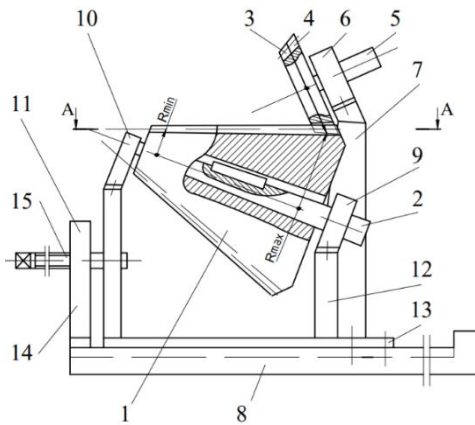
Одноступенчатый вариатор с коническими зубчатыми колесами
